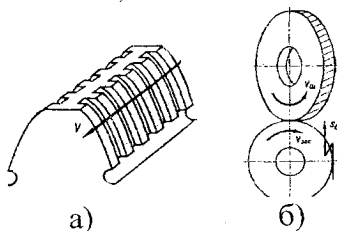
Зуб шевера та схема шевінгування зубців
